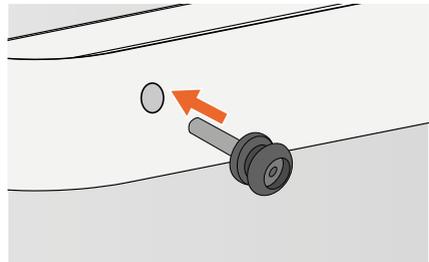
Befestigen der Schraube mit Schlaufenverbindung.
